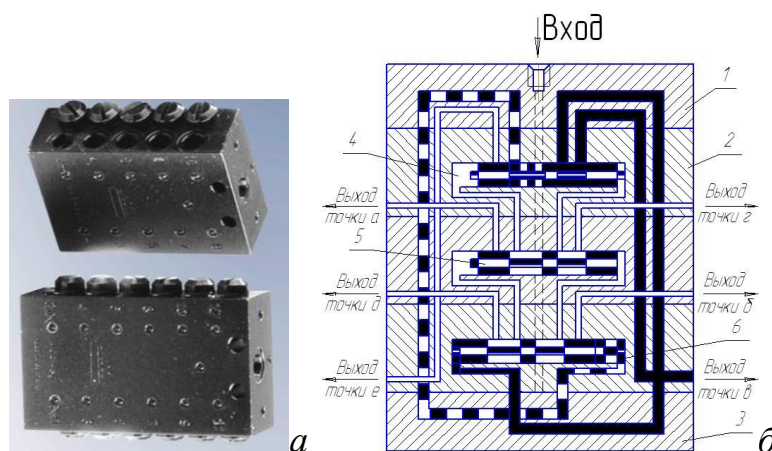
Общий вид однолинейного питателя (а), схема работы однолинейного питателя (б)
